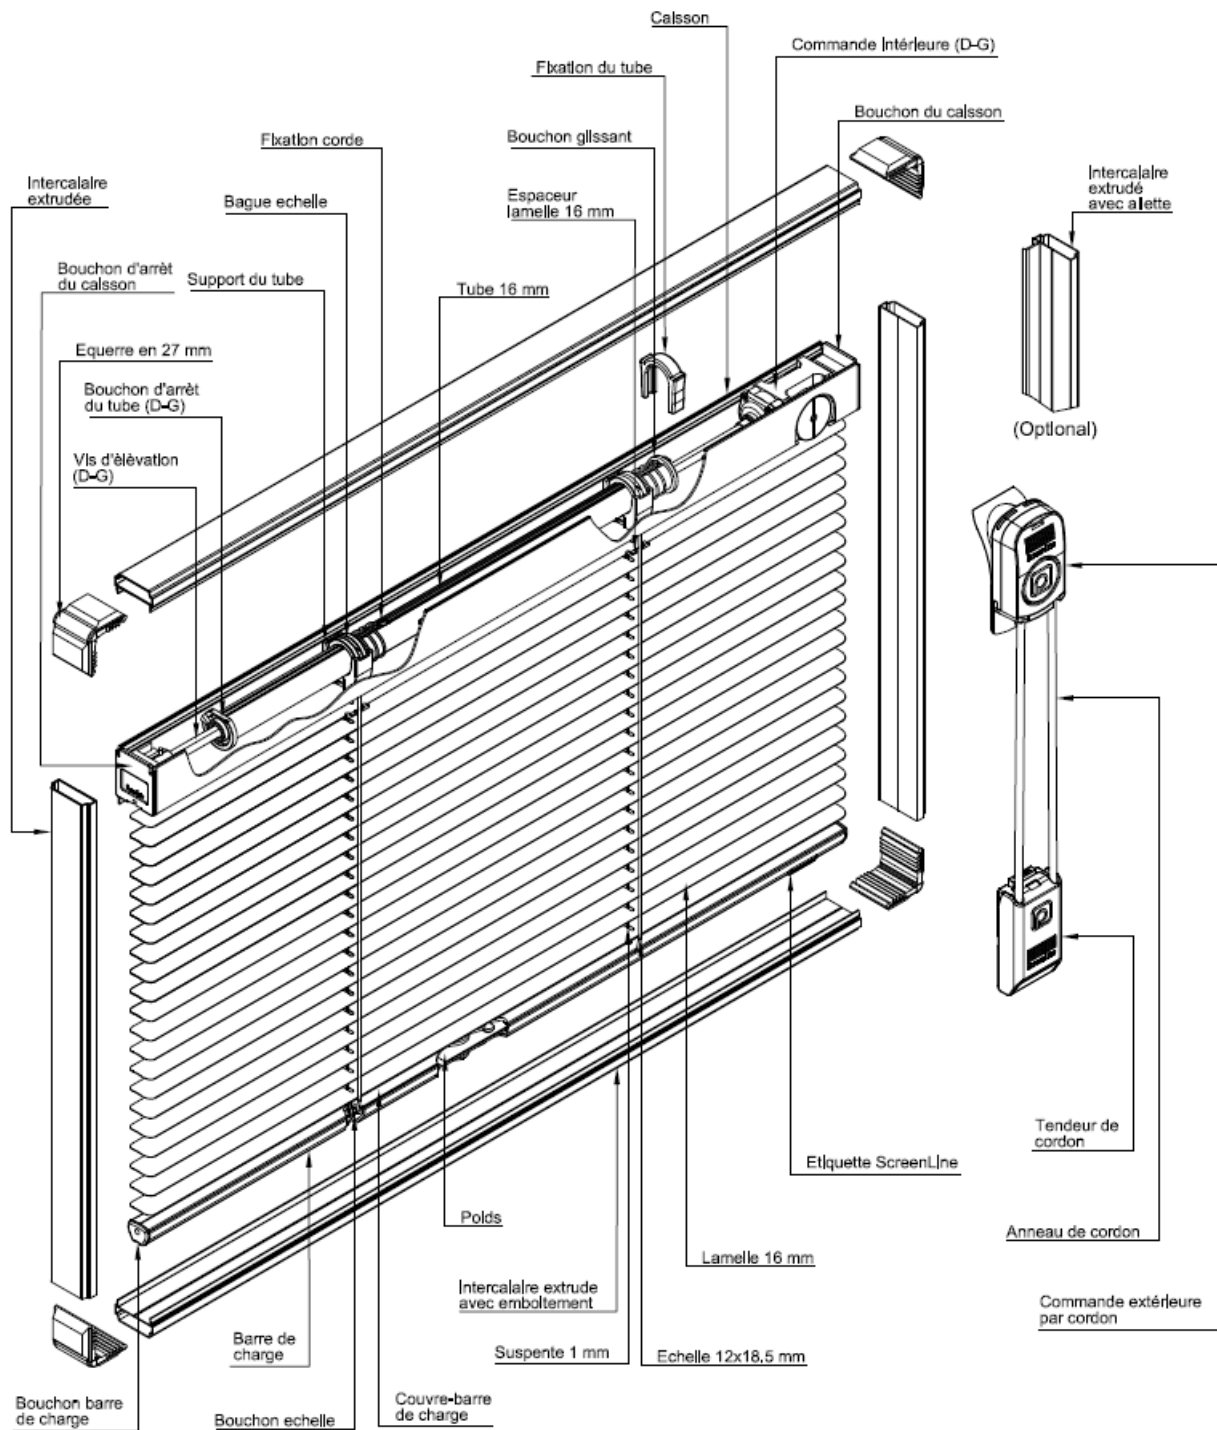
Vue d'ensemble éclatée – Store en position basse
